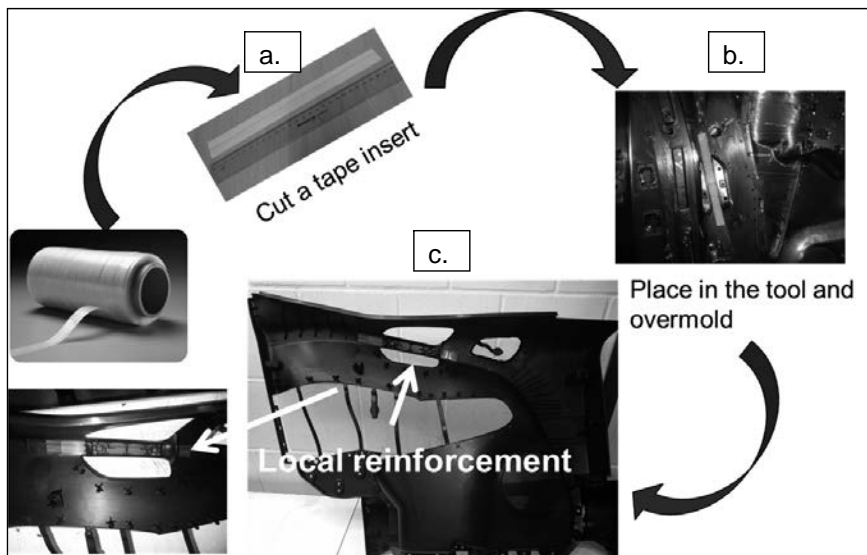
Stark vereinfachter Prozessablauf der „Lokalen Verstärkung“: a. Einleger werden zugeschnitten, b. Fixierung der Einleger auf der Werkzeugoberfläche, c. Bauteil mit lokaler Verstärkung wird dem Spritzgusswerkzeug entnommen. (Source: Celanese intern)
